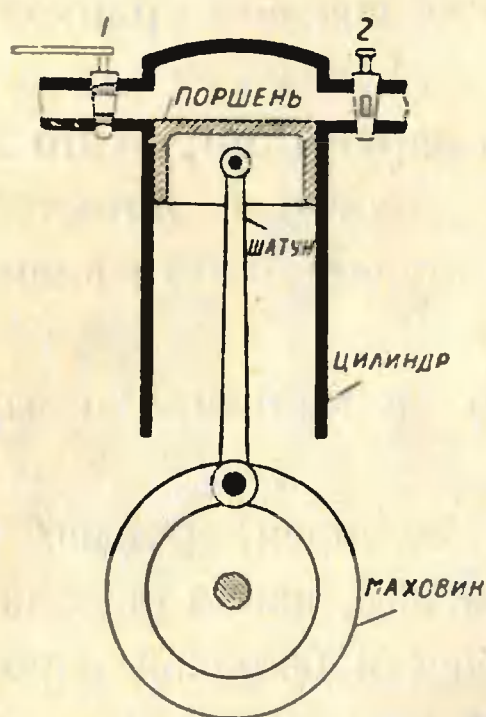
Как Гаврилов нарисовал разрез одного цилиндра двигателя.
